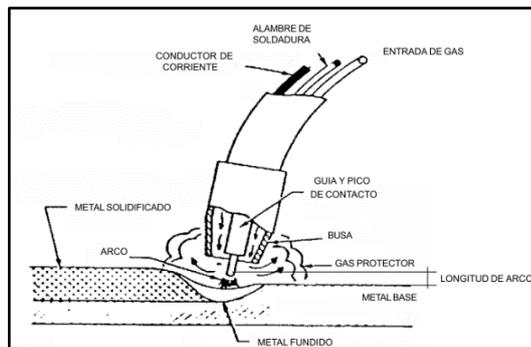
Esquema del proceso de soldadura MIG utilizado
